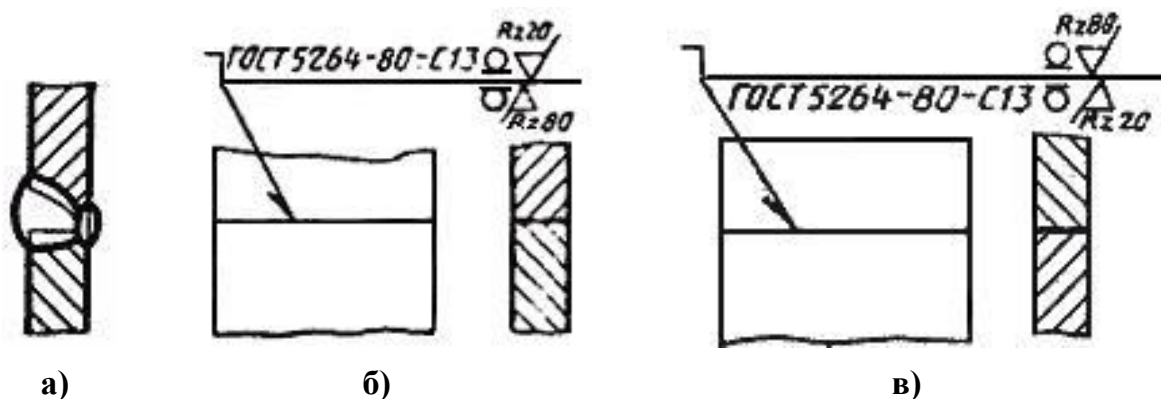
Пример обозначения сварного шва [5]: а – форма поперечного сечения шва; б – обозначение с лицевой стороны; в – обозначение с оборотной стороны
